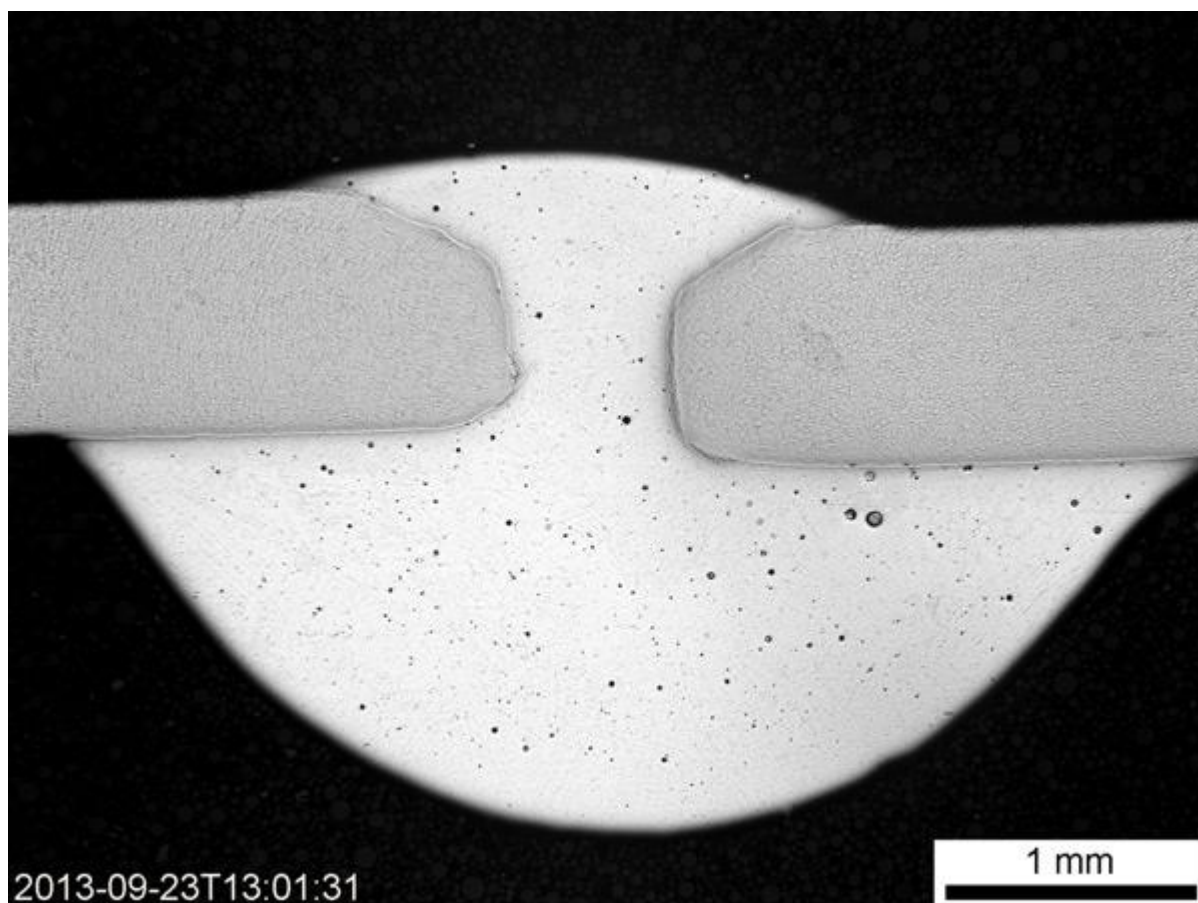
Una unión a tope de soldadura fuerte con arco protegido con gas. Fuente: TWI
